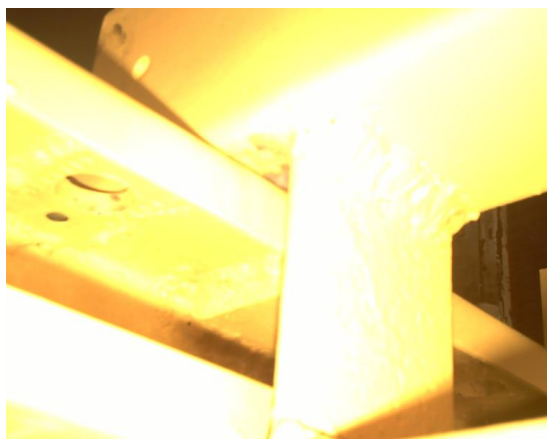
Unión de las vigas de la mesa de trabajo.
